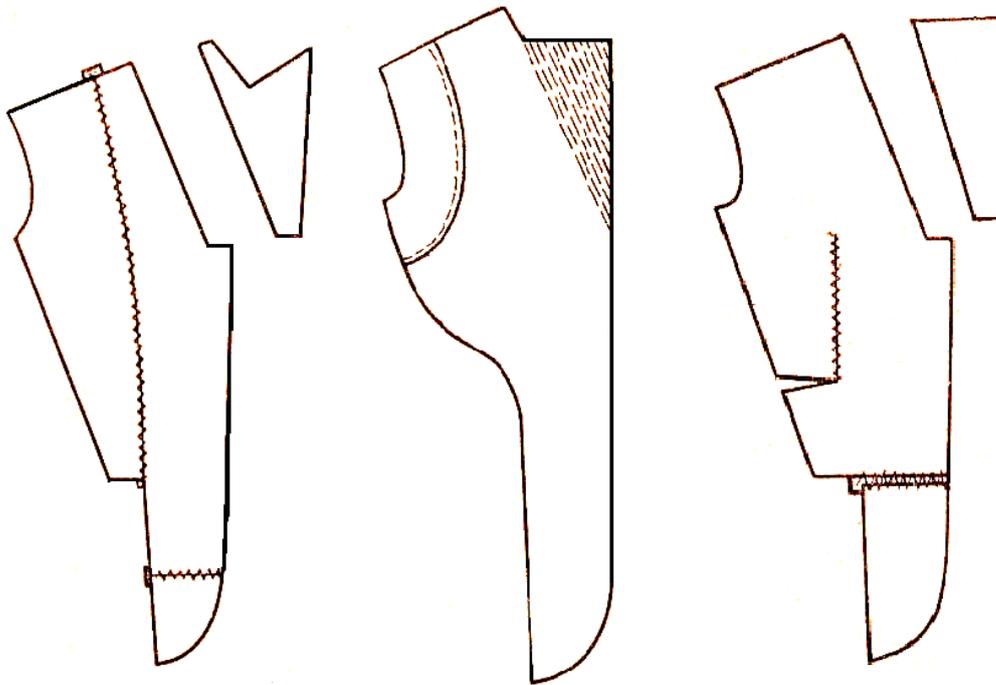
Заготовка бортовой прокладки ниточным способом.
